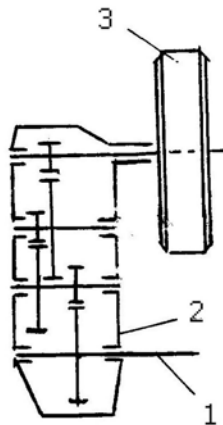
Индивидуальный двигатель: 1 – вал трансмиссии; 2 – редуктор; 3 – маховик
